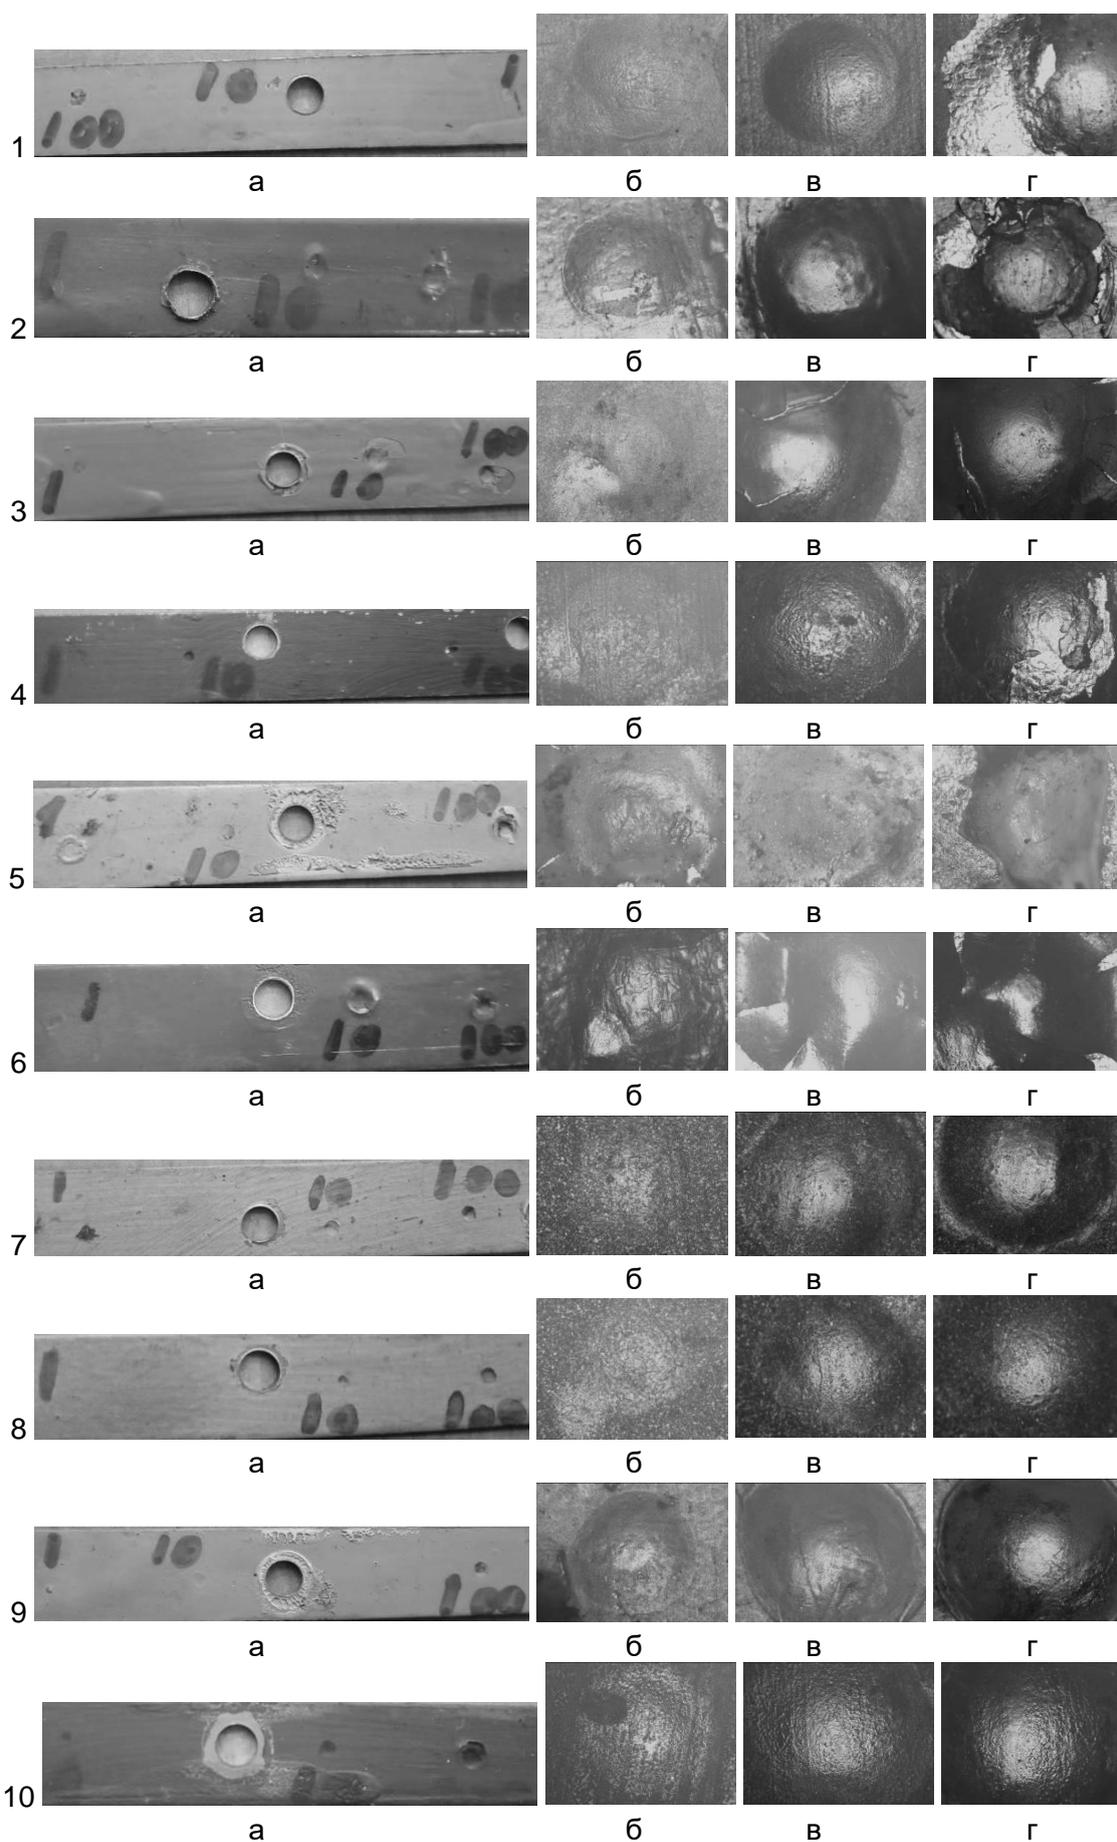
Металлические образцы после лабораторных испытаний (фото авторов): а – внешний вид образца; б – один удар; в – десять ударов; г – сто ударов
